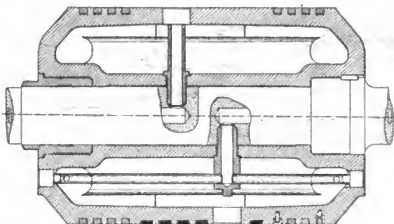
Kolben einer Körtingmaschine mit Weißmetallfütterung, ausgeführt von der Gutehoffnungshütte in Oberhausen.
